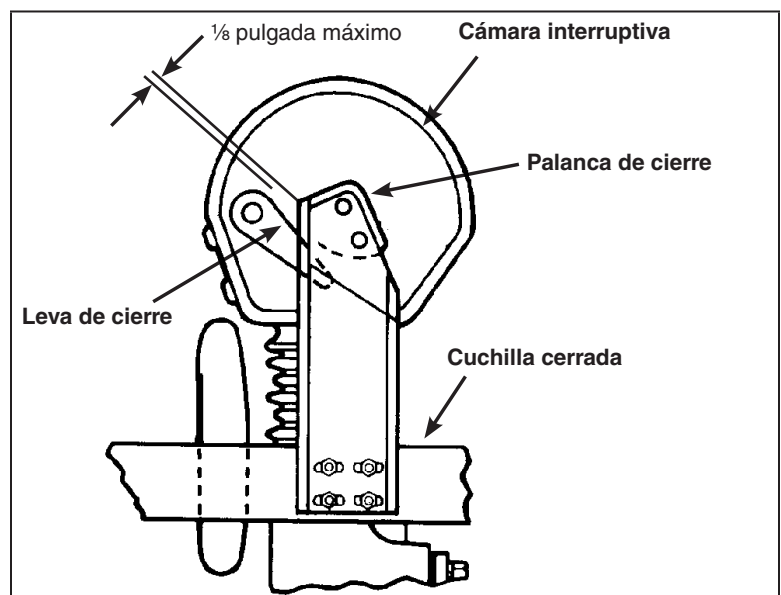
Conjunto de las cuchillas en posición de cierre total.
